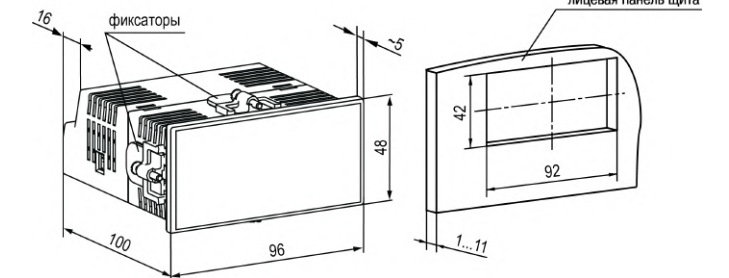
Габаритные размеры корпуса Щ2 и монтажного отверстия в щите
